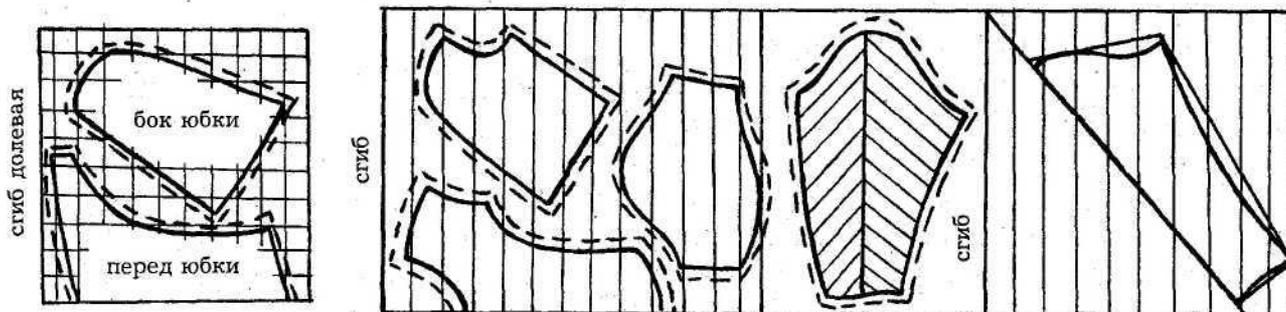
Раскладка выкроек на ткань в полоску и клетку с допусками на швы
